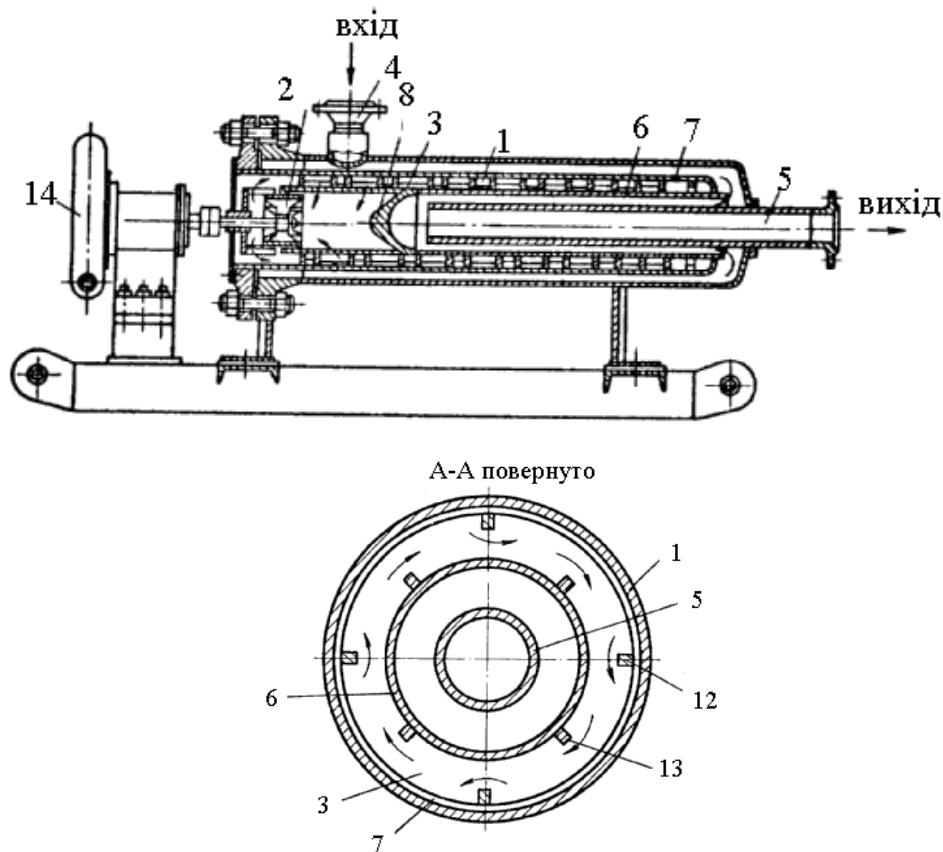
Пристрій для розігрівання газового середовища: 1 – корпус; 2 – привідне колесо; 3 – міжтрубний простір; 4, 5 - вхідний і вихідний патрубки; 6, 7 – труби теплообмінника; 8 – торець внутрішньої труби; 9 – гвинтові вставки; 10, 11 - ходи міжтрубного простору; 12, 13 – поздовжні ребра; 14 – привід колеса.
